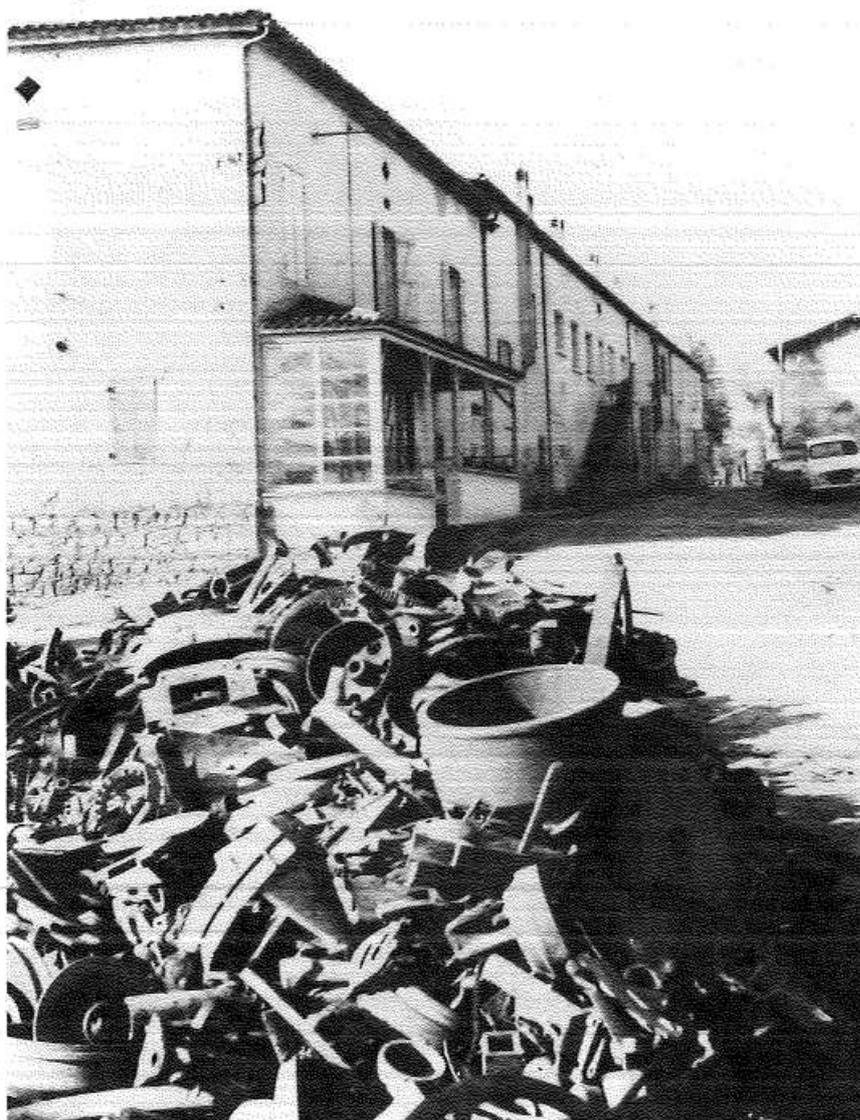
Logements ouvriers construits en 1848. A l'extrémité du bâtiment la terrasse couverte donnait accès aux bureaux de l'usine. Au premier plan, pièces de fonte de récupération destinées à être refondues.
